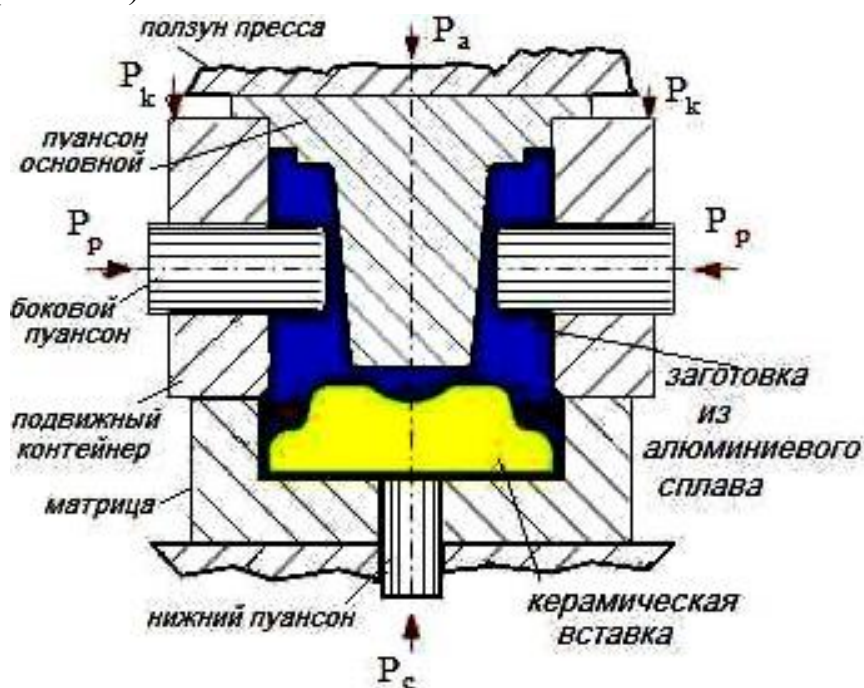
Схема жидкой штамповки композитного поршня
